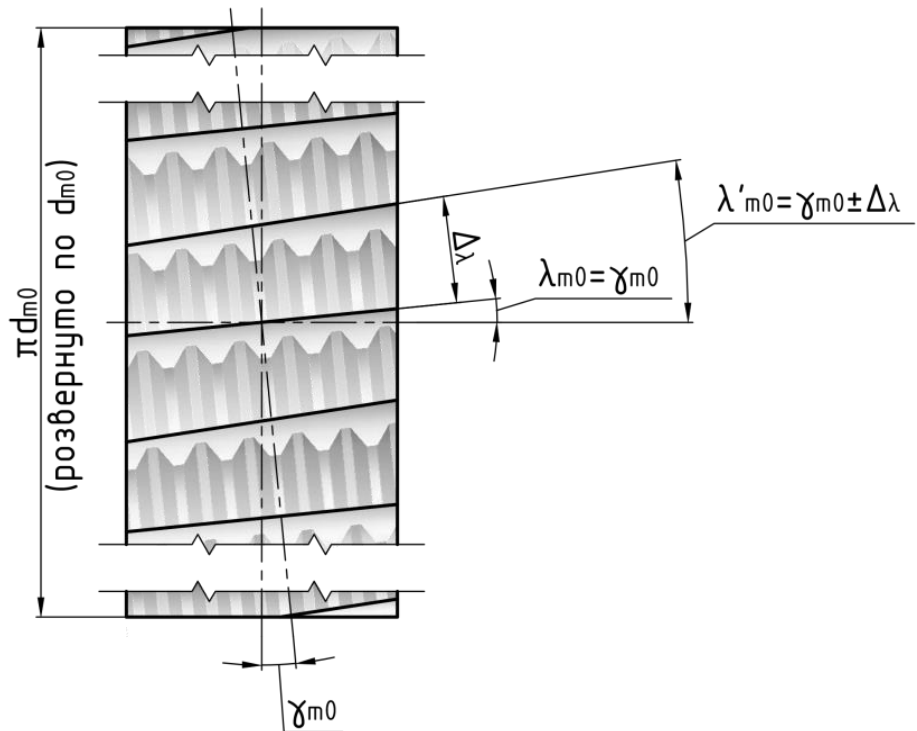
Принципова схема черв'ячної зуборізної фрези з чергуванням стружкових канавок різного нахилу
